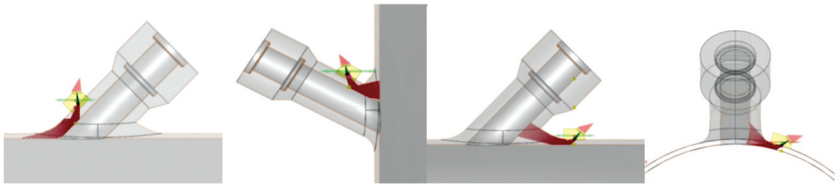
BOSS头焊缝及堆焊层 PAUT 检验仿真示意
